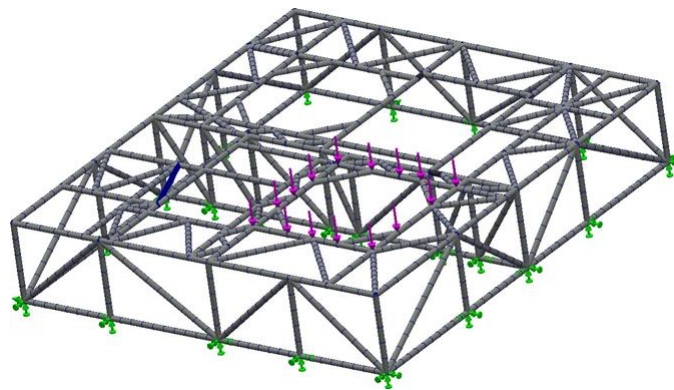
Estrutura metálica (Malha de 40 mm).
